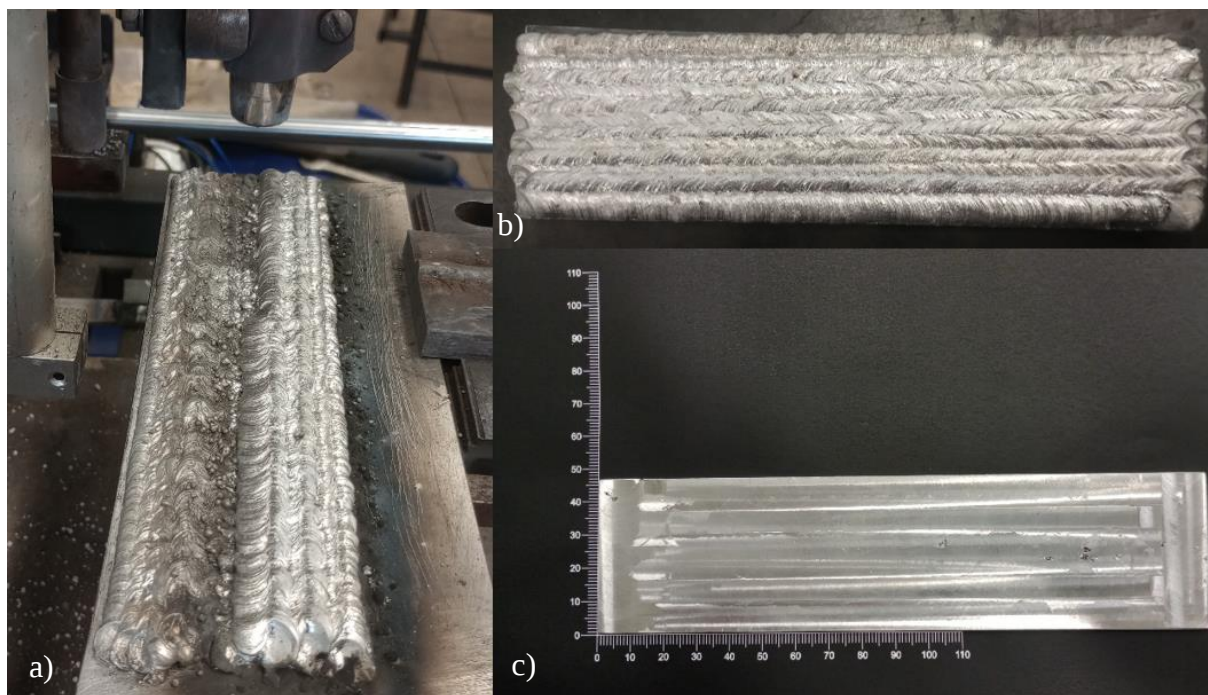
a) realização de soldagem sobre chapa, b) soldagem concluída e preparada para usinagem, c) chapa usinada pronta para extração dos corpos de prova para ensaio de tração e impacto.
